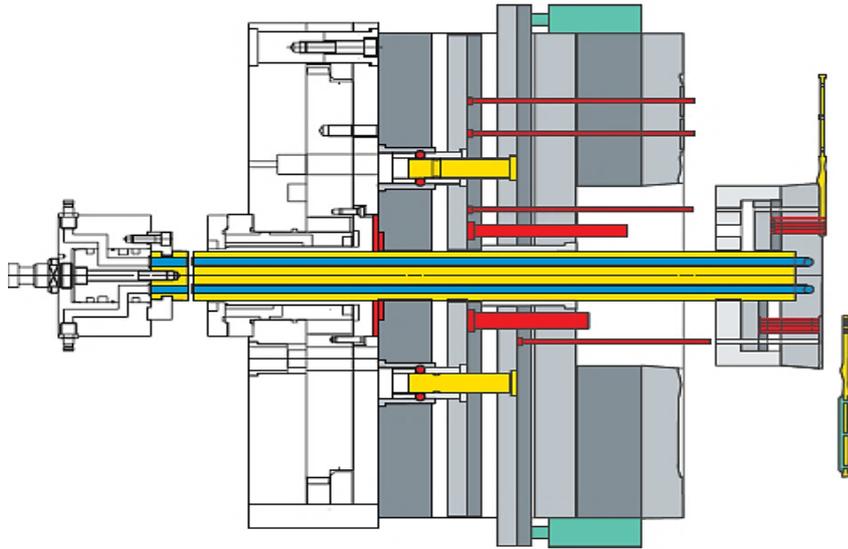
Molde bimatéria - rotação de um inserto do molde.
